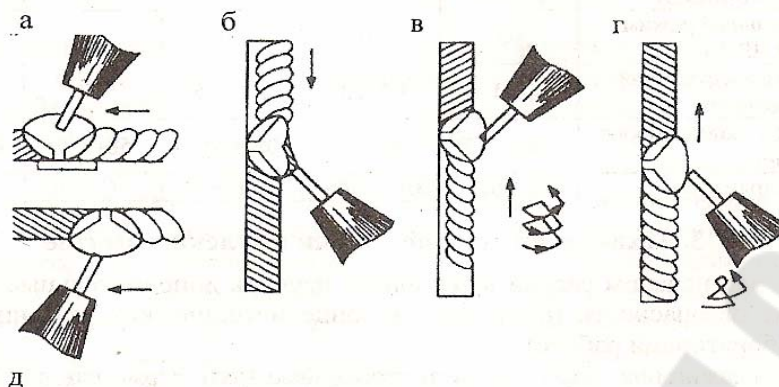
Схемы расположения шва и поперечные колебания электрода при полуавтоматической сварке в углекислом газе
